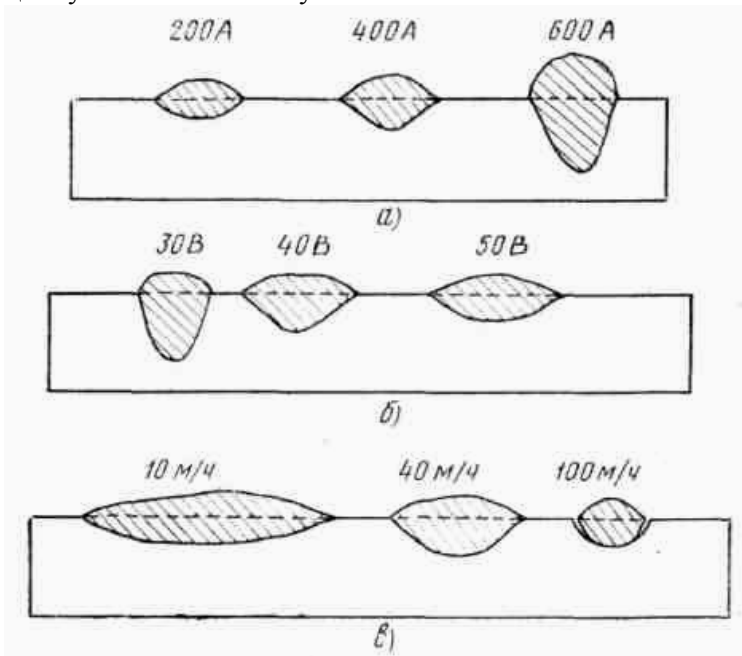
Вплив сили зварювального струму (*a*), напруги на дузі (*б*) і швидкості зварювання (*в*) на геометричні розміри й форму шва
